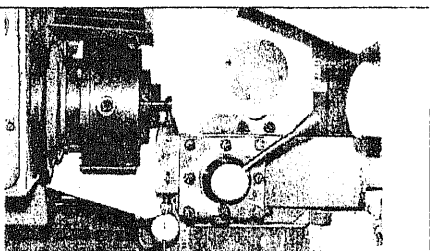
Настройка токарного станка для алмазного выглаживания цилиндрического участка рабочей поверхности круглого резца
